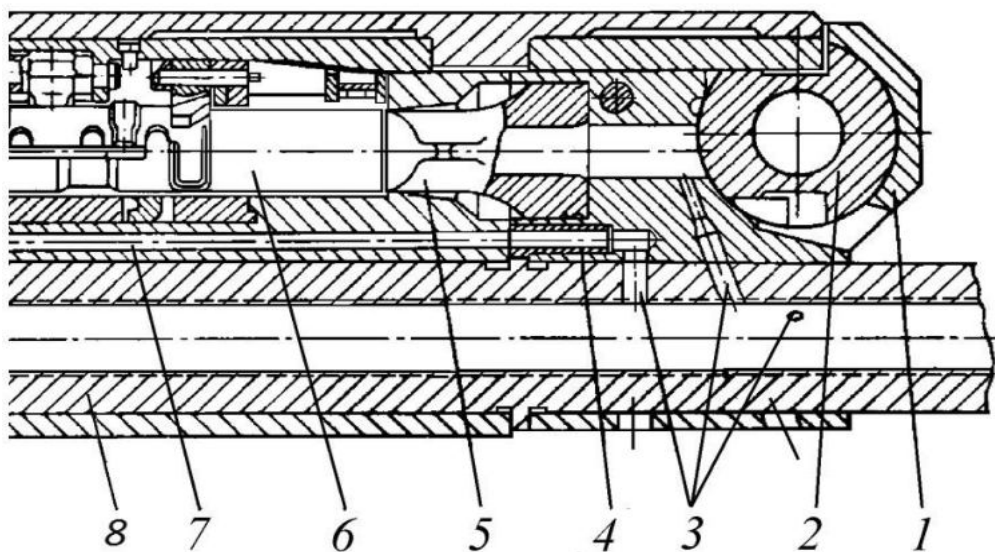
Газовые двигатели привода блока патронников и досылания патрона: 1 – корпус газовой камеры; 2 – поршень газового двигателя привода блока патронников; 3 – газоотводные отверстия; 4 – обтюратор пороховых газов газового выбрасывателя стреляных гильз; 5 – поршень-досылатель патрона; 6 – патрон; 7 – газоотводный канал выбрасывателя стреляных гильз
